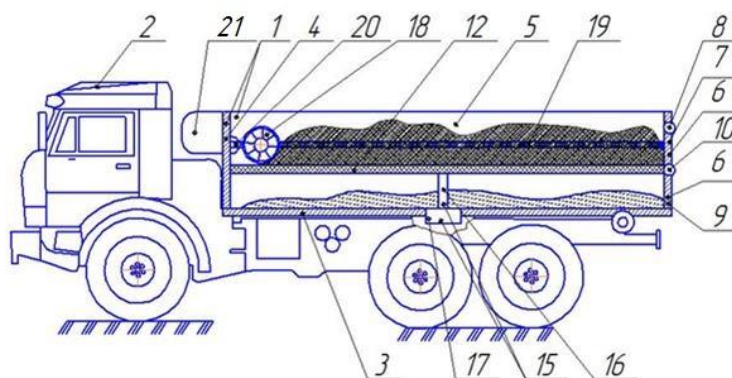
Схема конструкції молотильного пристрою люцерни на базі автомобіля: 1 – кузов; 2 – транспортний засіб; 3 – дно кузова; 4 – передній борт; 5 – бічні борти; 6 – задній борт; 7 – верхня частина заднього борту; 8 – шарнір; 9 – нижня частина; 10 – шарнір; 11 – гідроциліндр; 12 – перфорована гнучка мембрана (дека-решета); 13 – акумулятор; 14 – сітка; 15 – вібропривід; 16 – кінематичний зв'язок вібратора та дека-решета; 17 – вібратор; 18 - обмолочувальний барабан; 19 – напрямні; 20 – лебідка, 21 – акумуляторна батарея.
